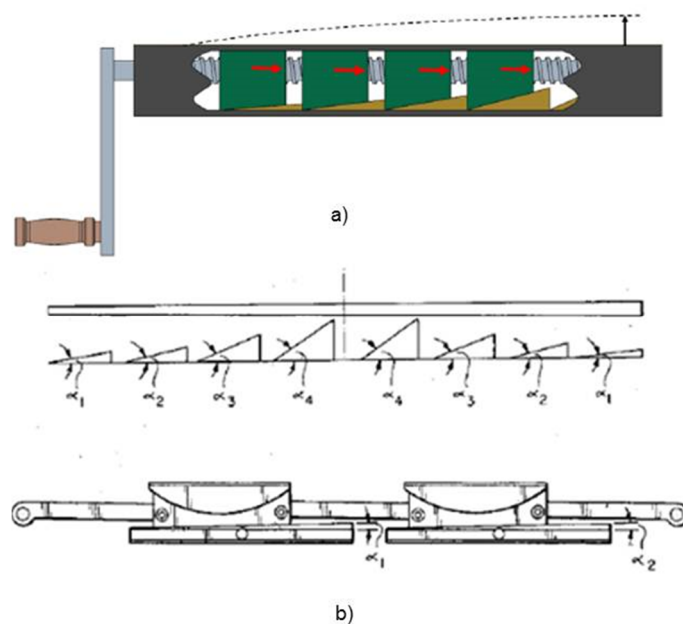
a) Mesa bombeada [32]; b) Pormenor de uma mesa bombeada [23]
